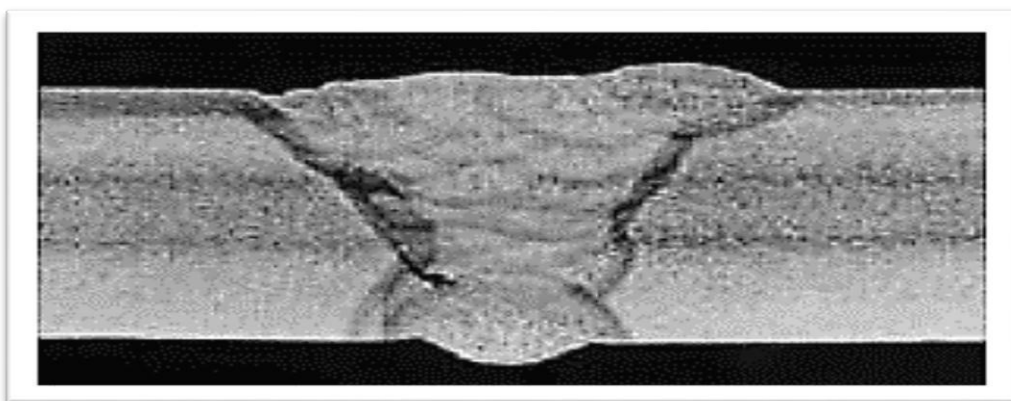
Manque de fusion dans le flanc de la soudure [27].
